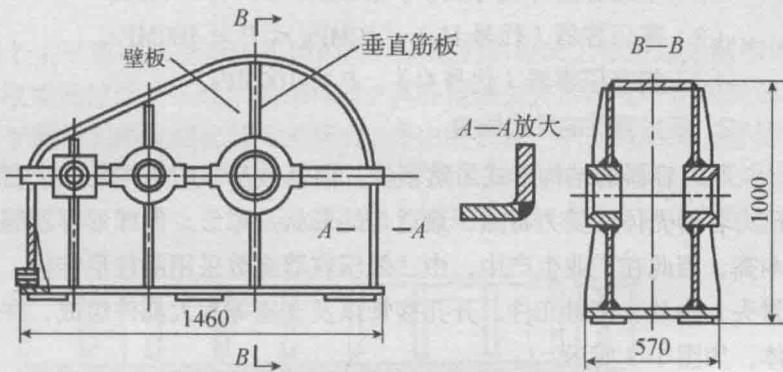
单壁剖分式减速器箱体焊接结构
